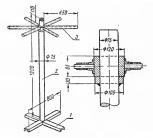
Вешалка для камер: 1 — основание; 2 — стойка; 3 — звездочка.
